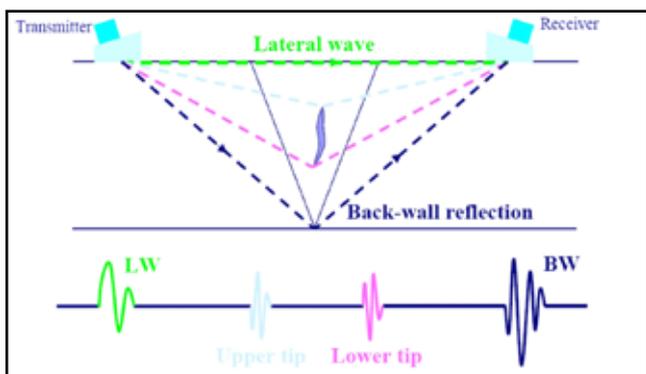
Configuración básica en una inspección de soldadura mediante la técnica TOFD y señales más representativas.
